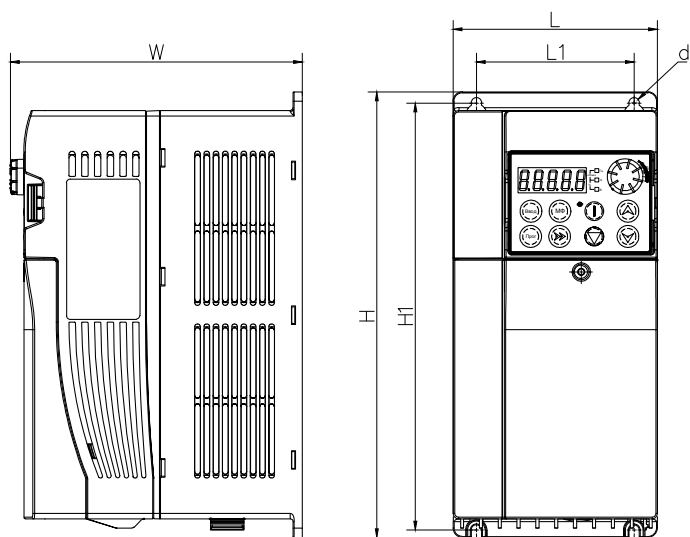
Габаритные и установочные размеры преобразователя (габарит 3)
